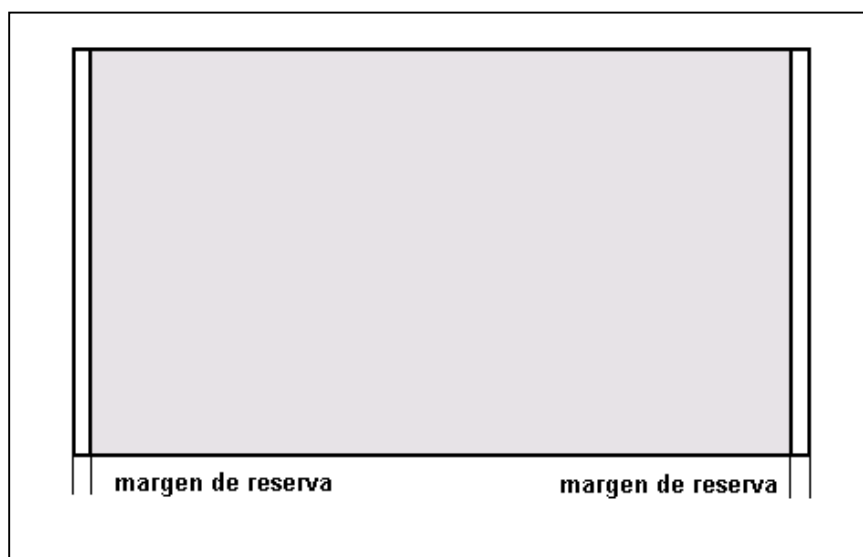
Sistema principal de soldado por resistencia de envases metálicos en su parte lateral.
